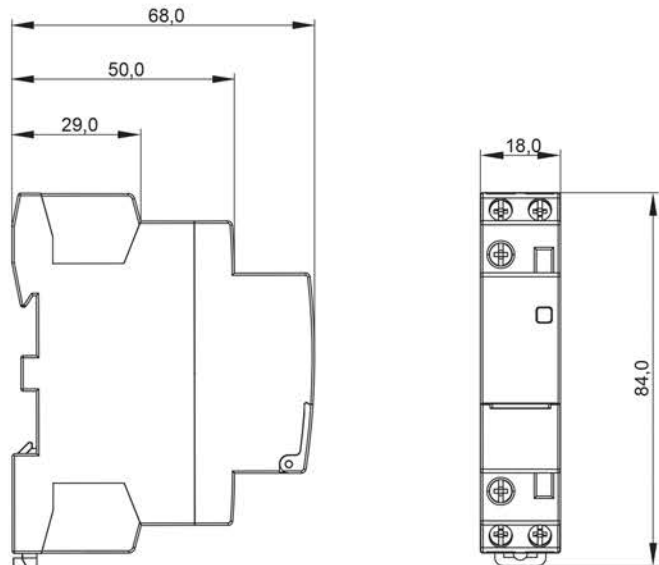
Габаритные размеры контакторов до 25 А, 2P / Figure 1 – Overall dimensions of contactors up to 25 A, 2P
